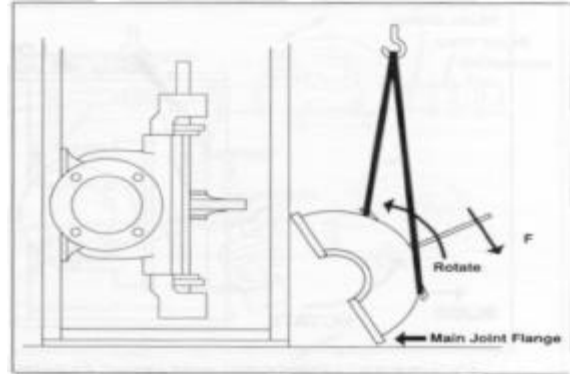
REMOCION DE MITAD SUPERIOR
